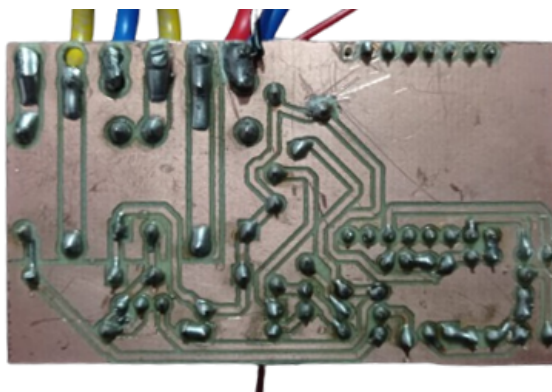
Soldadura de componentes en placa tomacorriente.
